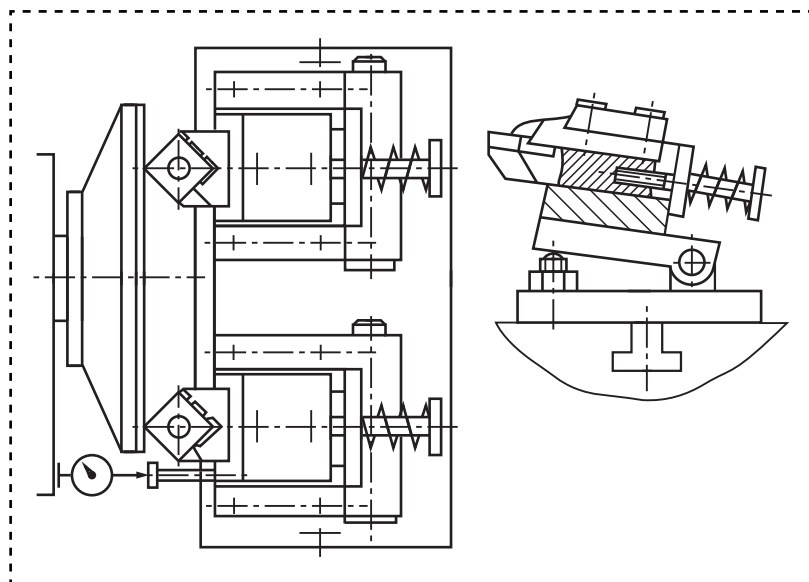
Двухпозиционное приспособление для заточки твердосплавных пластин
